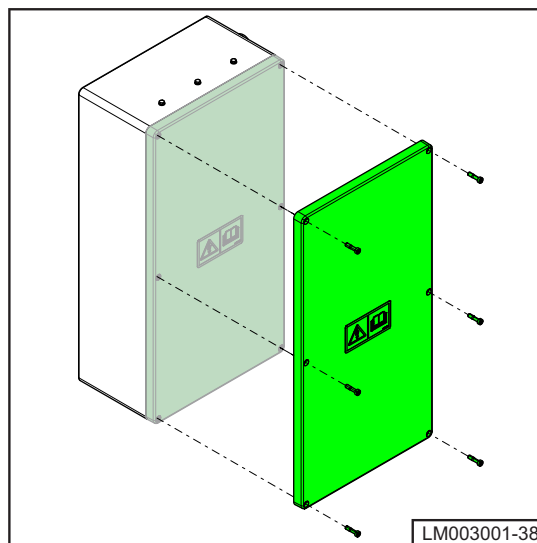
Fjerne bakre hydraulikkslangedeksel
